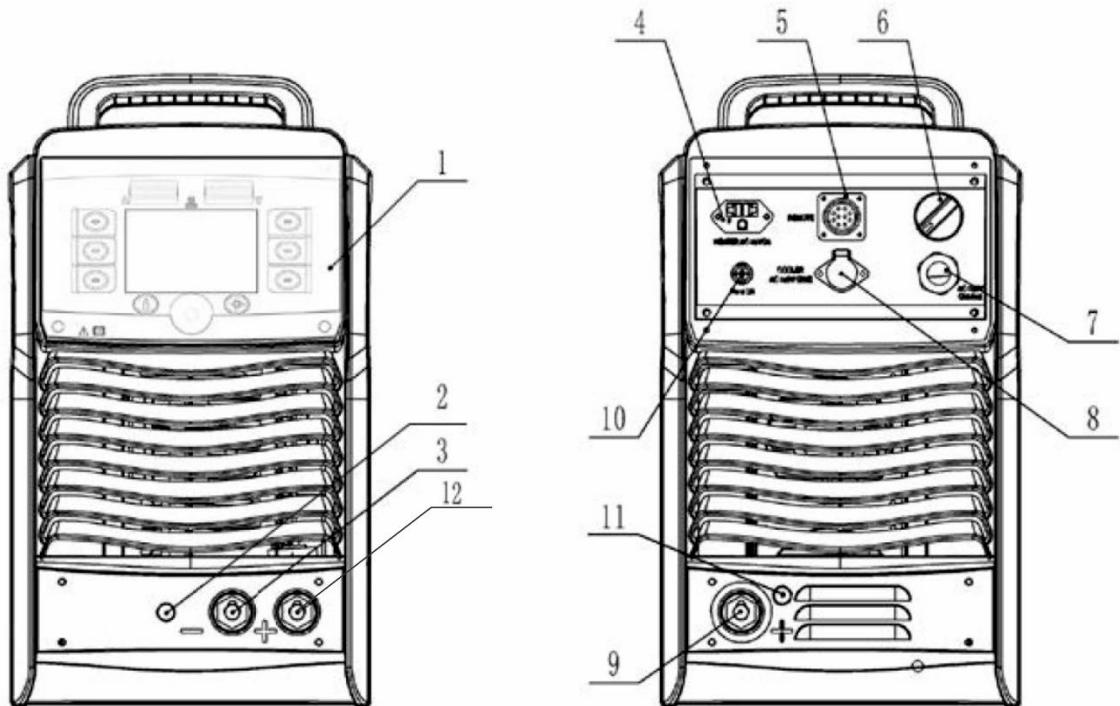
Общий вид сварочного аппарата (источника) спереди/сзади
